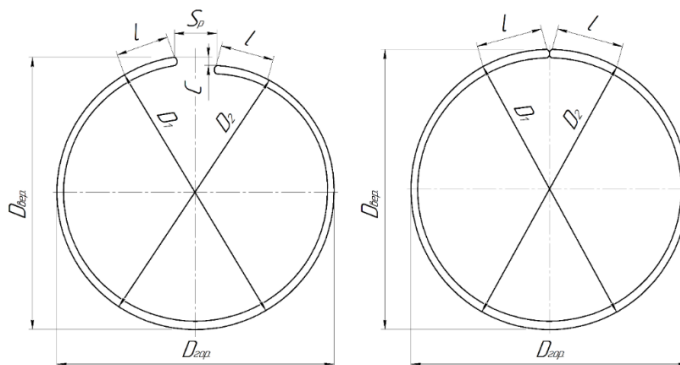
Схема измерения геометрии заготовки после формовки – экспандирования
